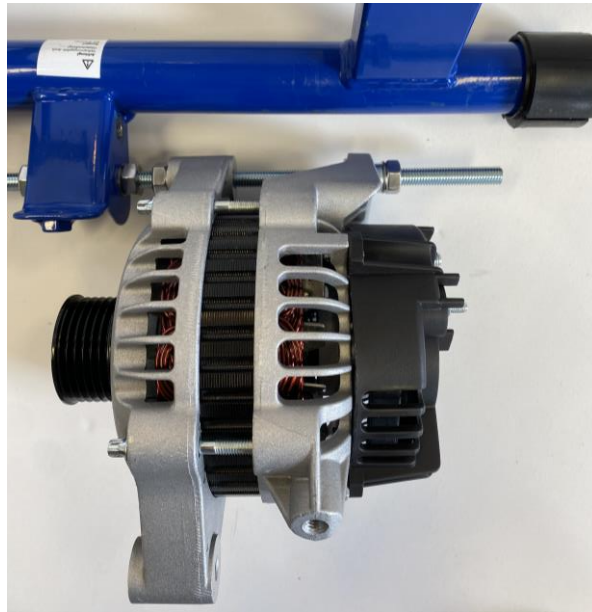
Montage der Lichtmaschine auf der Gewindestange
